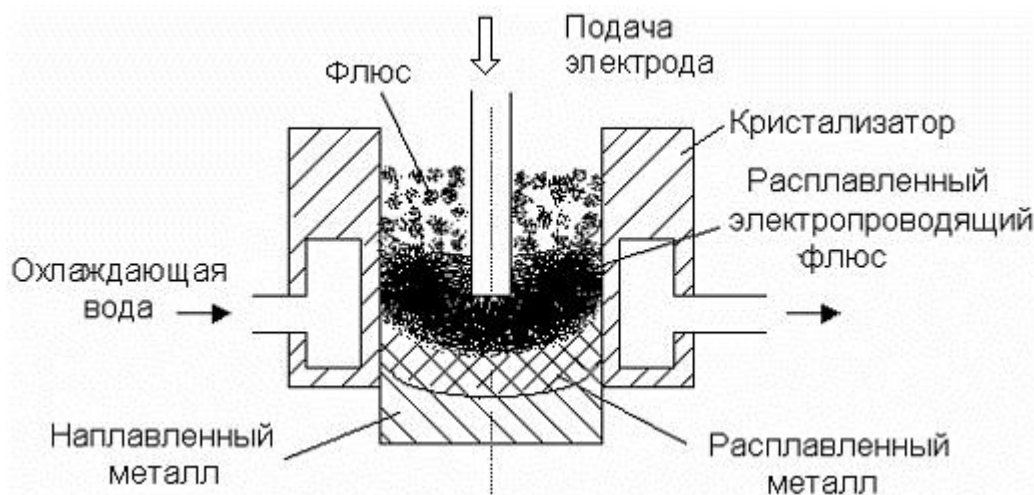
Схема электрошлаковой сварки
